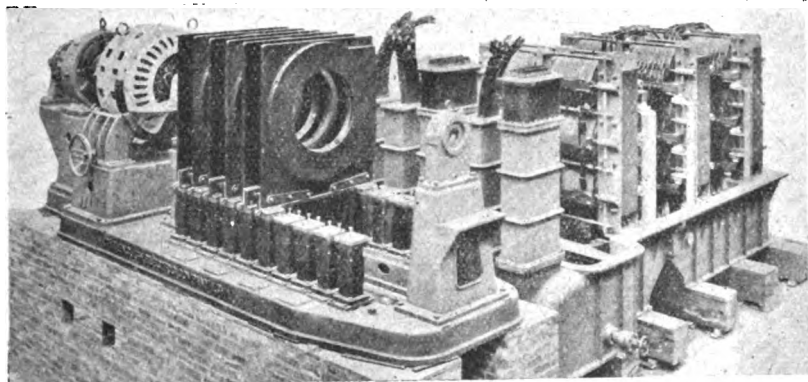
Vista della macchina, durante il montaggio, dalla parte del collettore.
